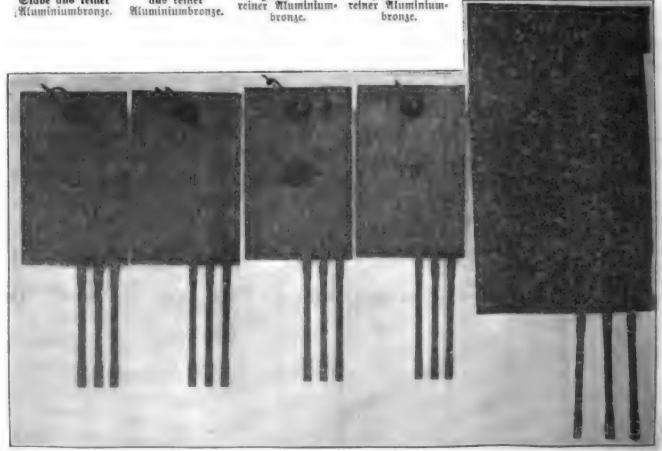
Platte aus Rupfer, Stabe aus reiner Aluminiumbronge.
